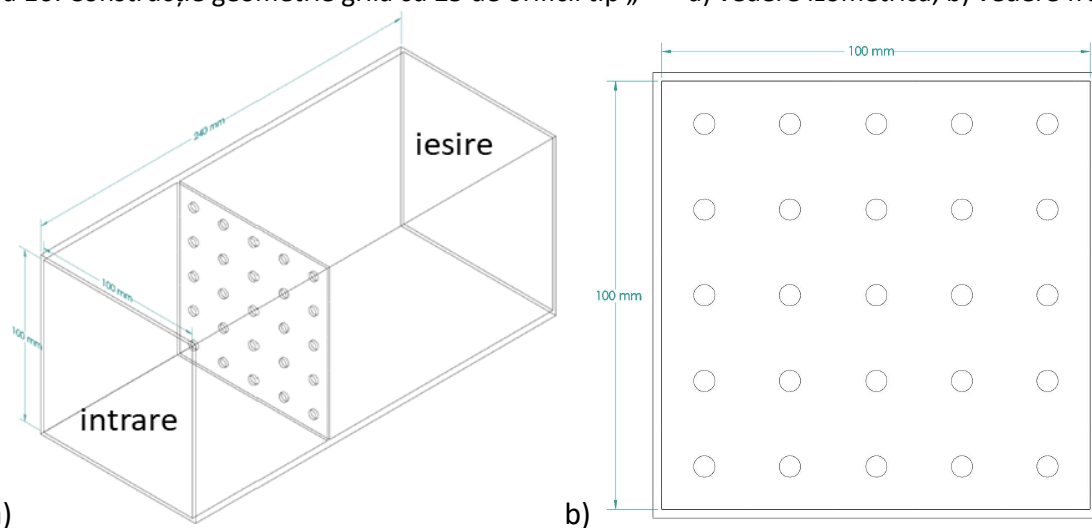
Construcție geometrie grilă cu 25 de orificii tip „O” - a) vedere izometrică, b) vedere frontală
